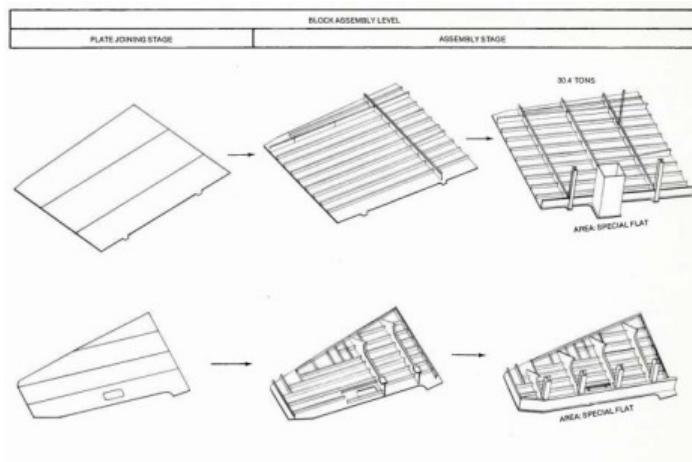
Block Assembly and Grand-block Joining. Corrugated Transverse Bulkhead and Deck Center Between Cargo Holds
